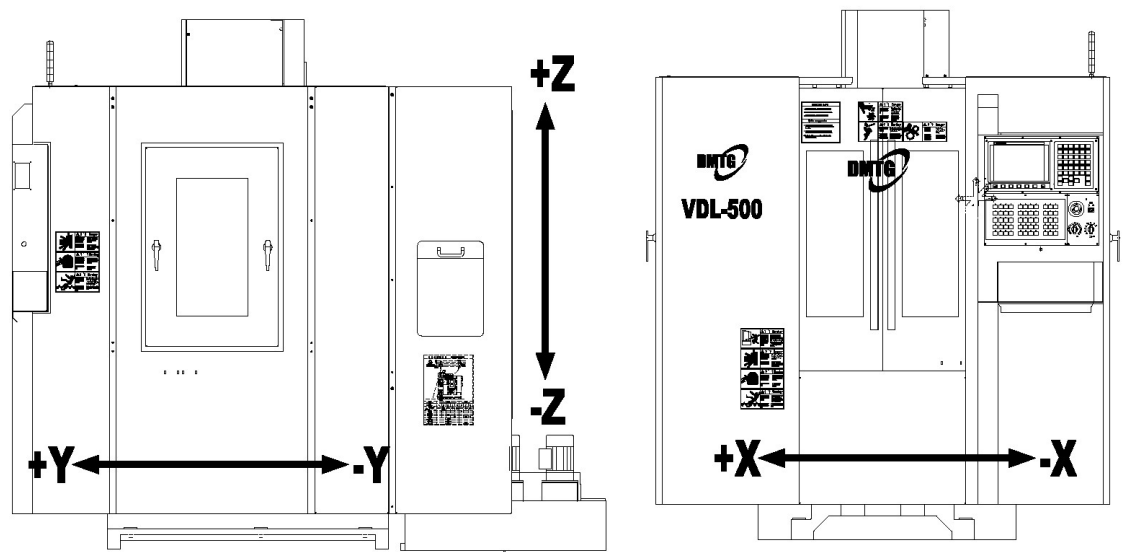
Зовнішній вигляд вертикального обробного центру.
